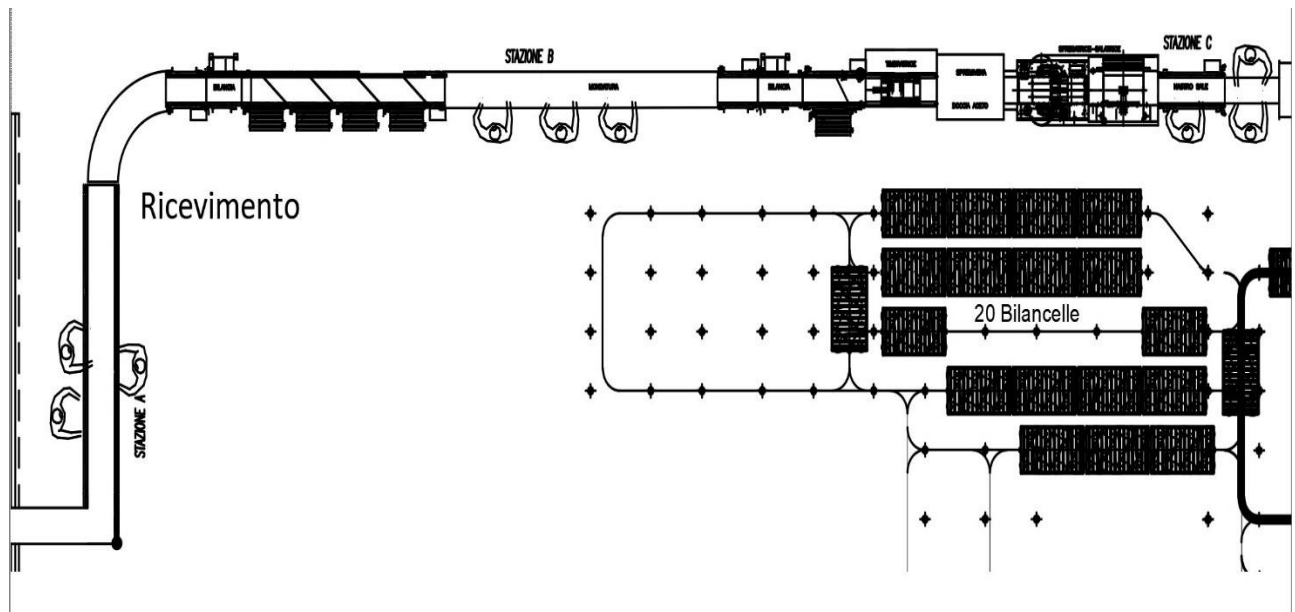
Layout parziale dell'impianto stazioni A+B+C
